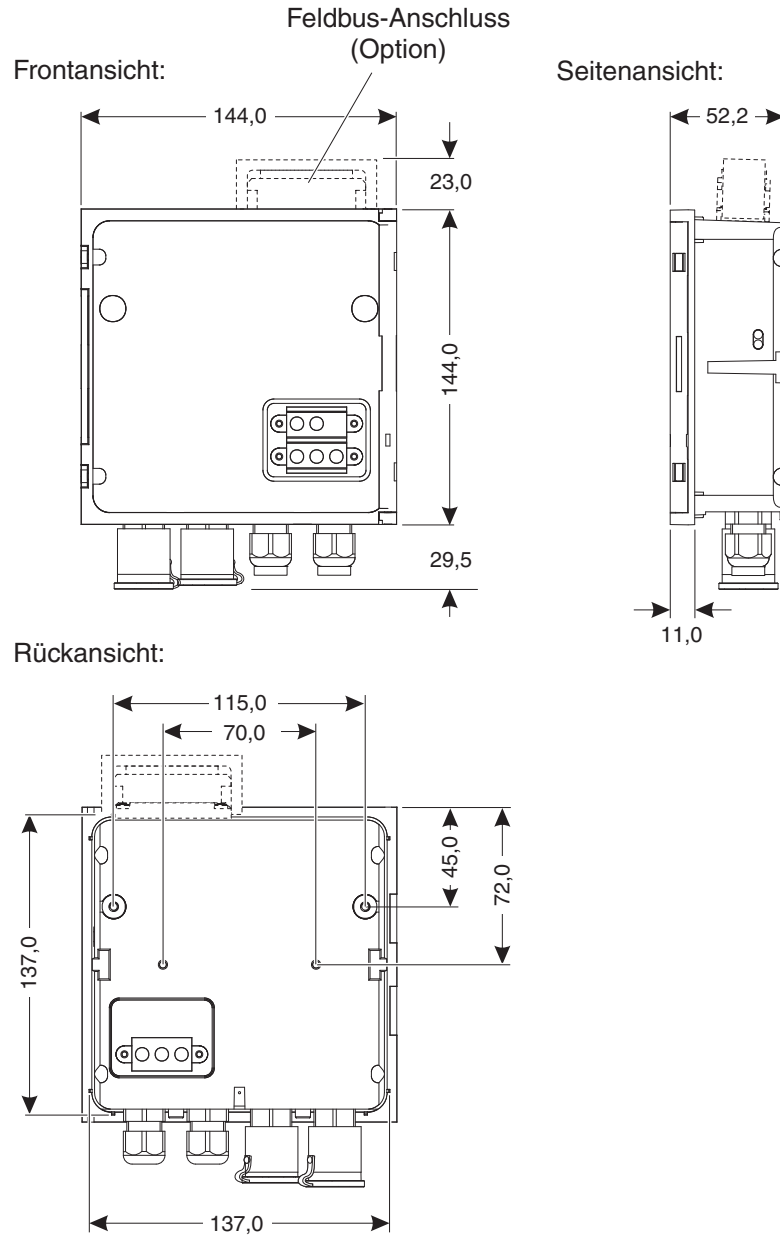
Maßzeichnung MIQ/MC3 (Maße in mm)
